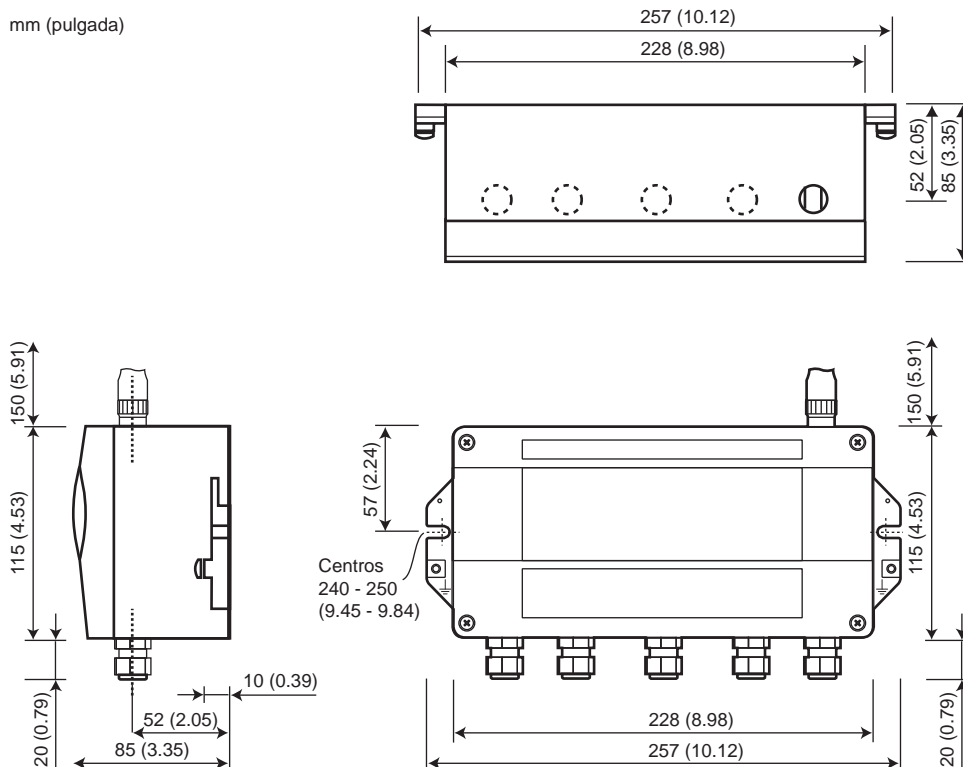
Dimensiones de Wireless Fieldgate SWG70
